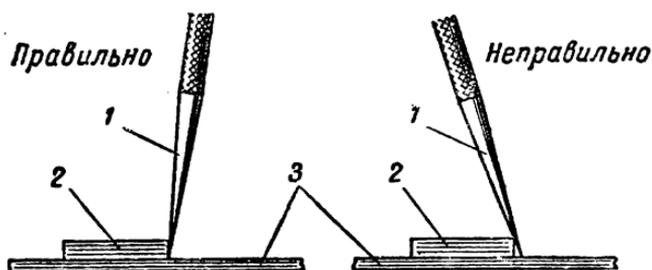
Положение острия чертилки при разметке. 1—чертилка; 2—угольник, линейка или шаблон; 3—размечаемая заготовка.
